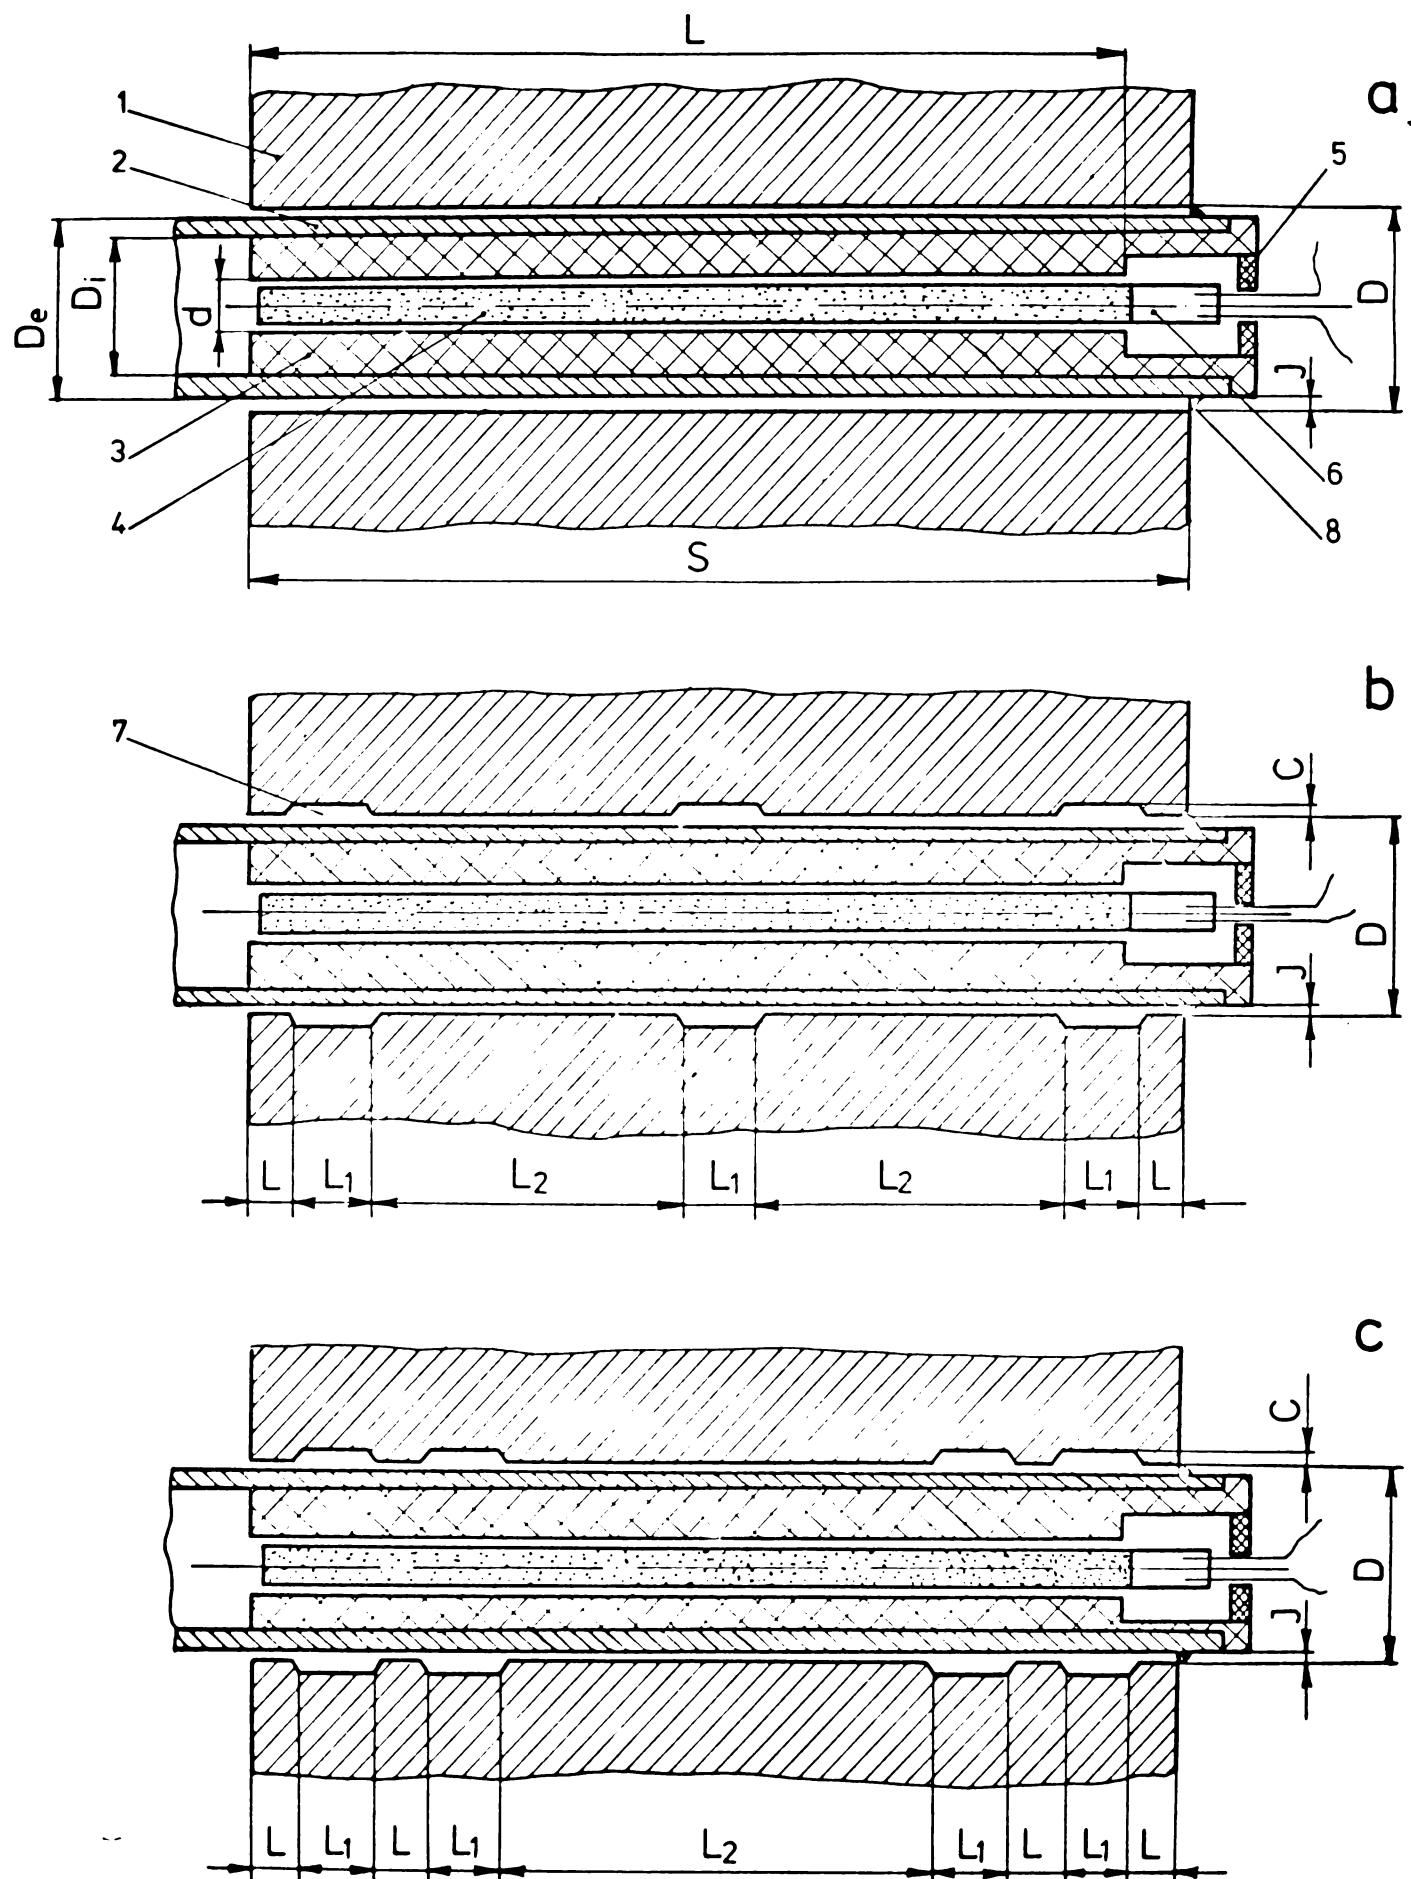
Geometria de mandrinare - sudare prin explozie a ţevilor la plăcile tubulare.
